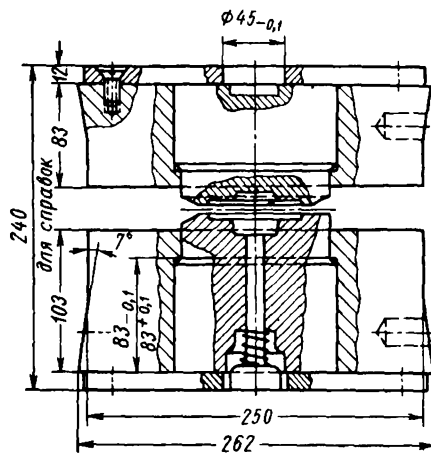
Цилиндрические вкладыши в сборе с призматической державкой
